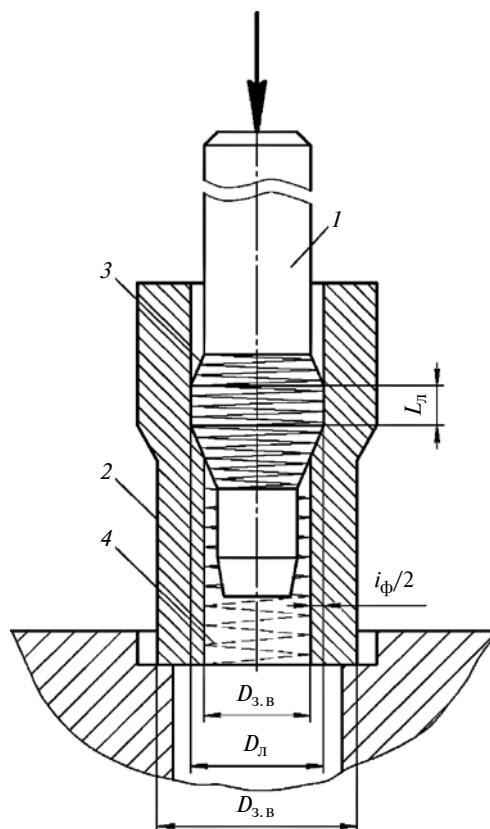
Схема дорнования отверстия полых цилиндрической заготовки:
